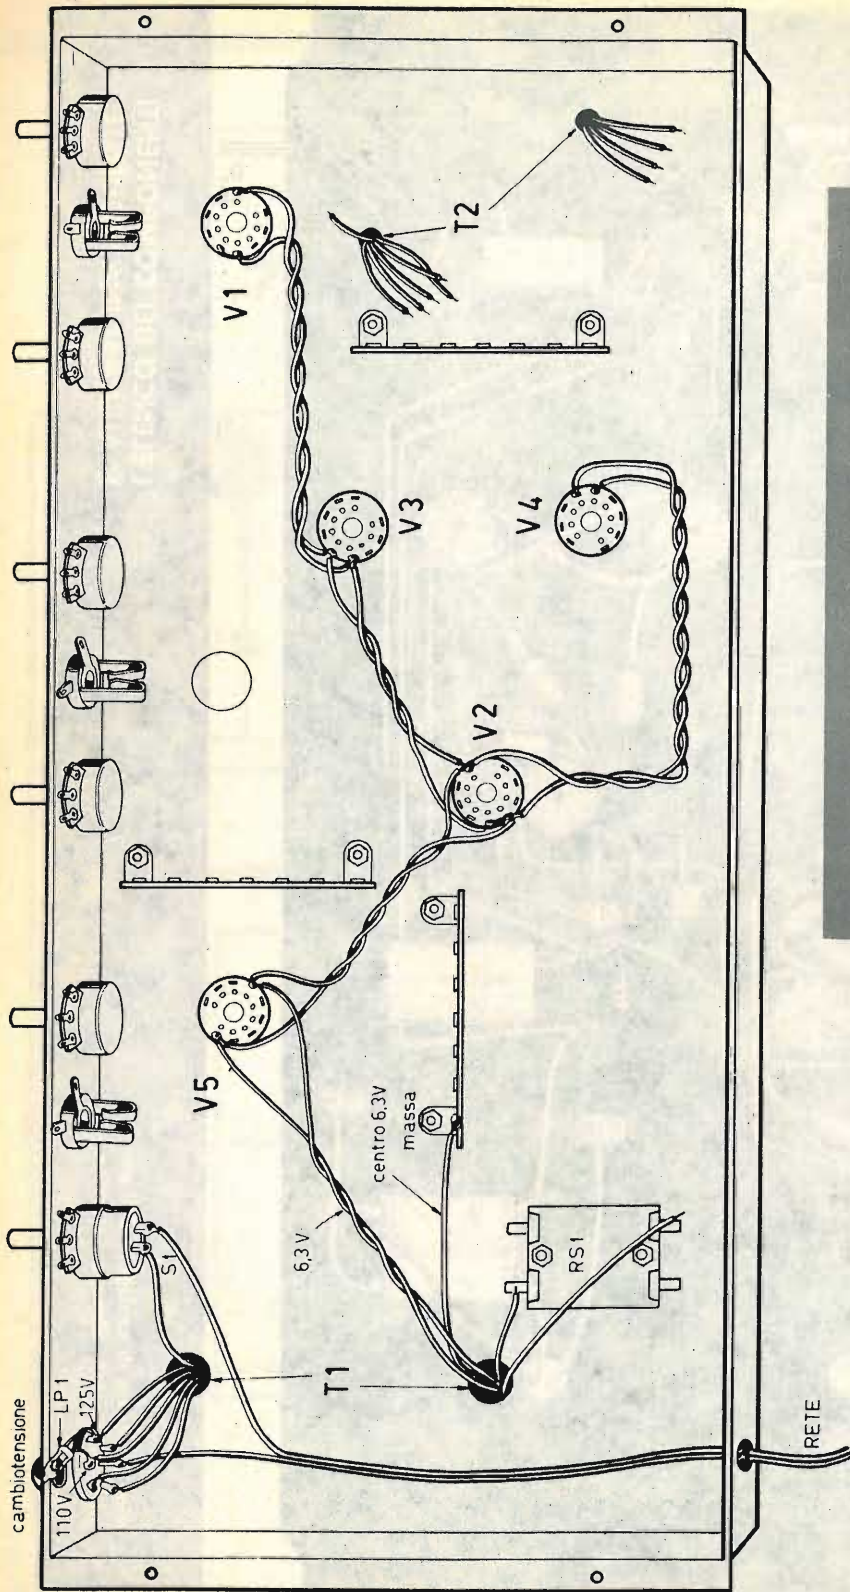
Piano di montaggio iniziale dell'amplificatore per chitarra elettrica.
